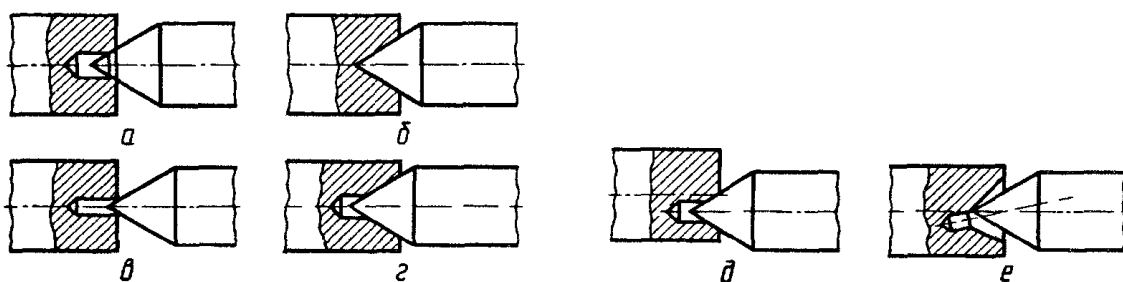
Неполадки, що виникають під час центрування торців заготовки вала
